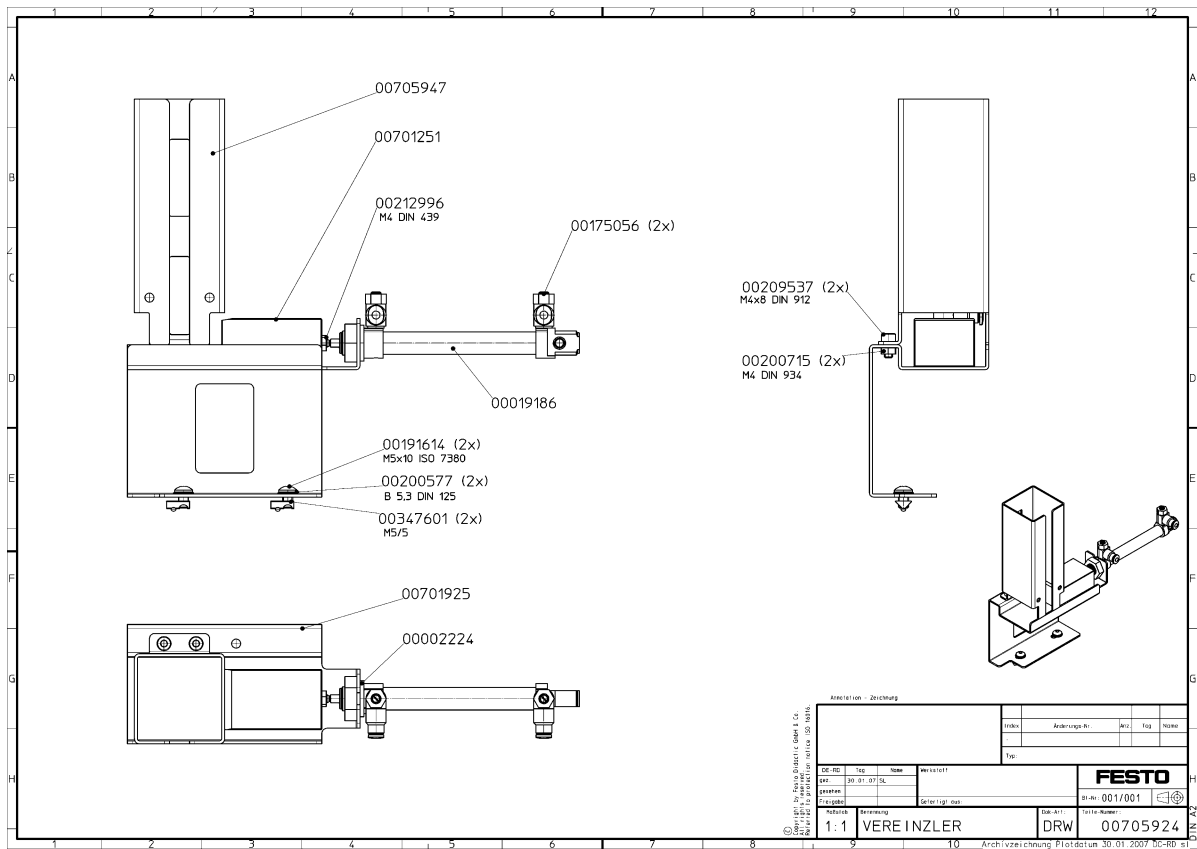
plan d'assemblage d'un chargeur-empileur (format d'origine : A3)
